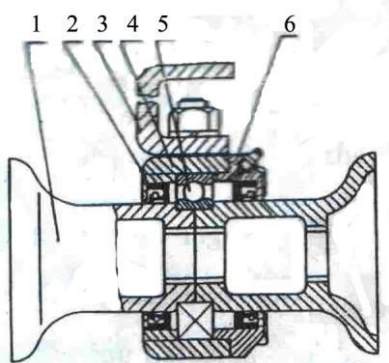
Присоединительный кронштейн с корпусом подшипников
